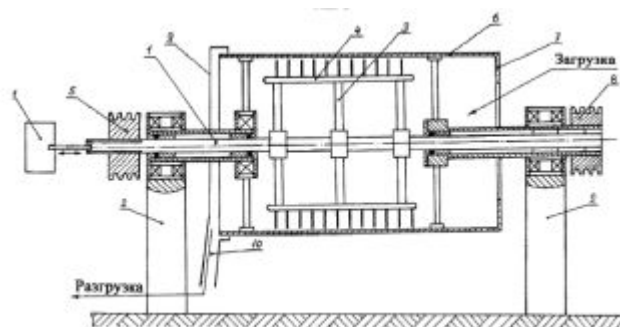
Схема центробежного смесителя роторного типа непрерывного действия
